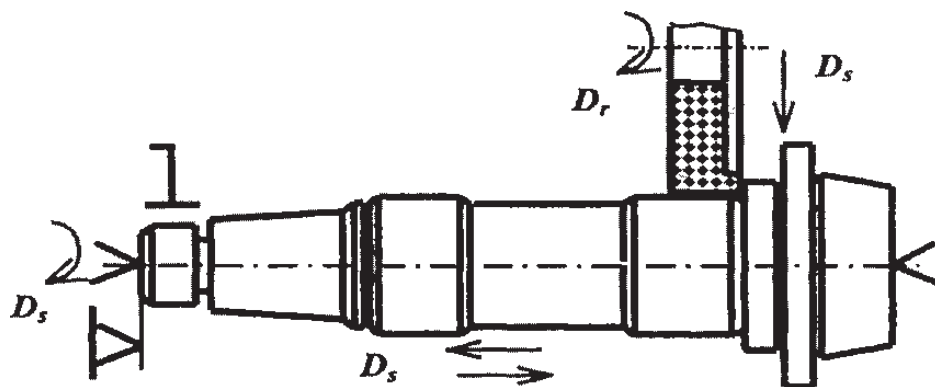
Схема обработки цилиндрической поверхности с одновременной подшлифовкой прилегающего торца шлифовальным кругом с выточкой
